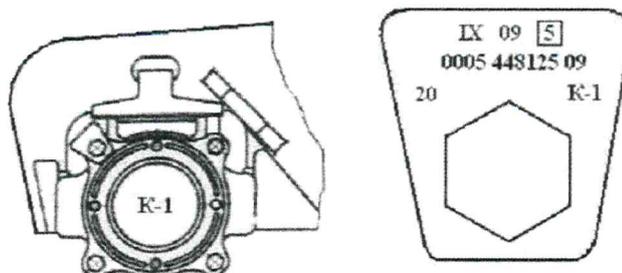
Внешние отличительные признаки буксового узла с подшипником кассетного типа в габаритных размерах 130x250x160 мм торговой марки BRENCO (EPK- BRENCO) в корпусе буксы
